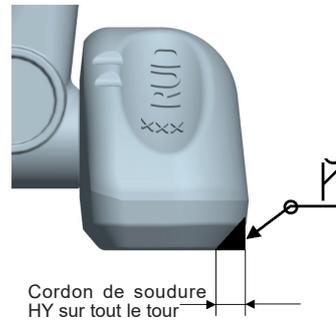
Cordon de soudure HY / HY-weld seam
